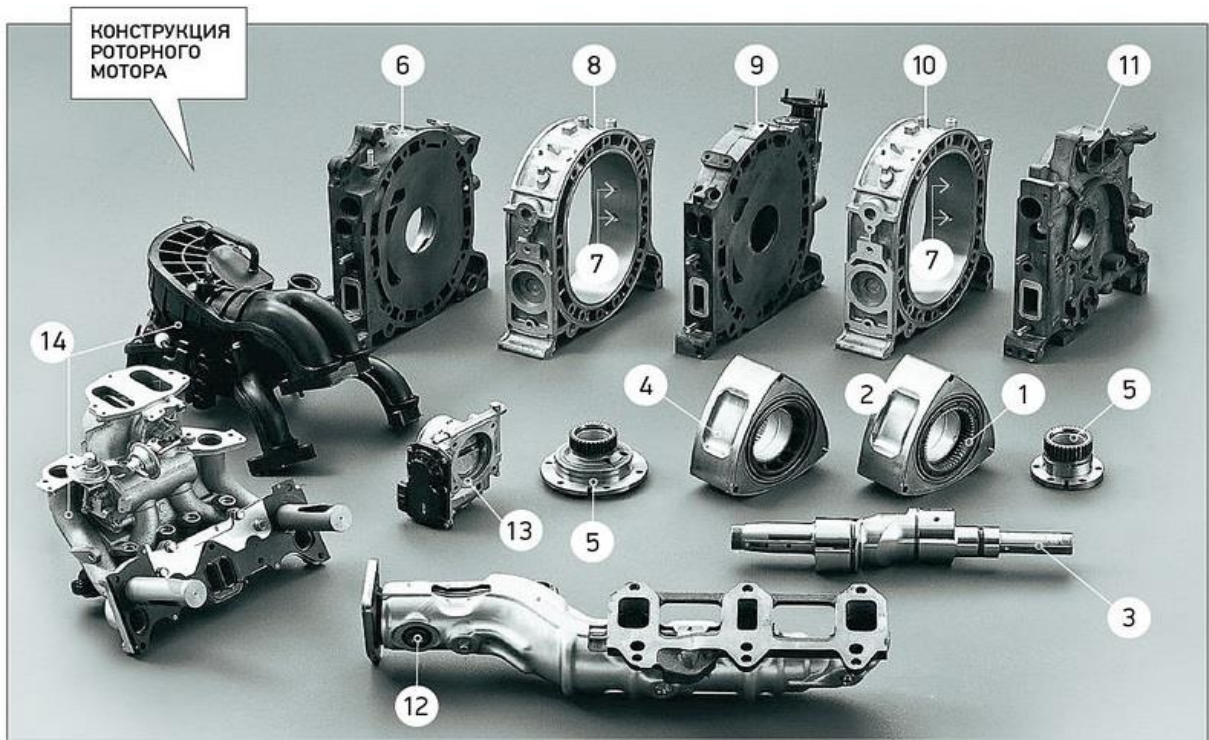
Конструкция роторно-поршневого двигателя внутреннего сгорания.
